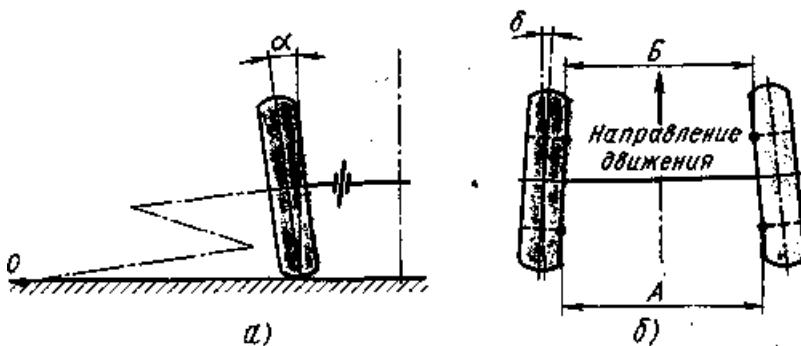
Углы установки управляемых колес: а — развал; б — схождение
